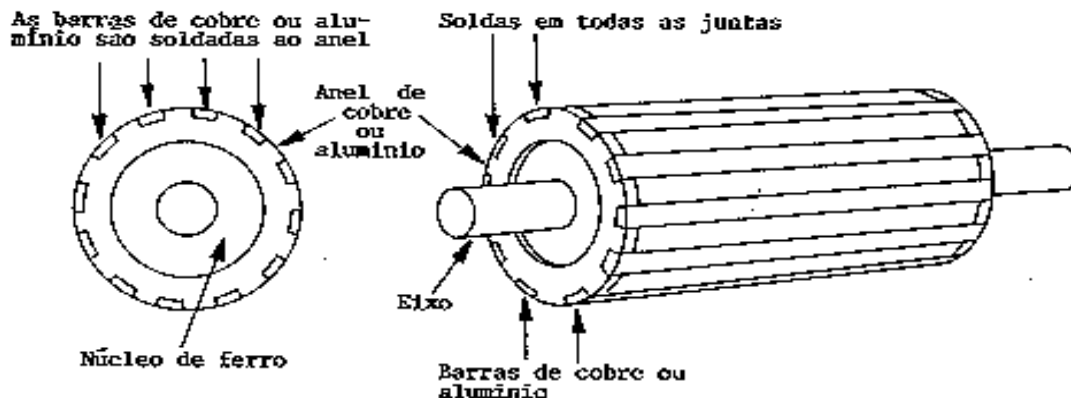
Rotor tipo gaiola para um motor CA de indução.
